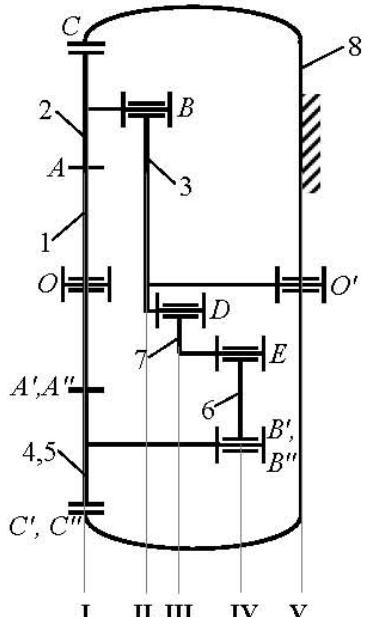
Трехсателлитный планетарный механизм в профильной плоскости
